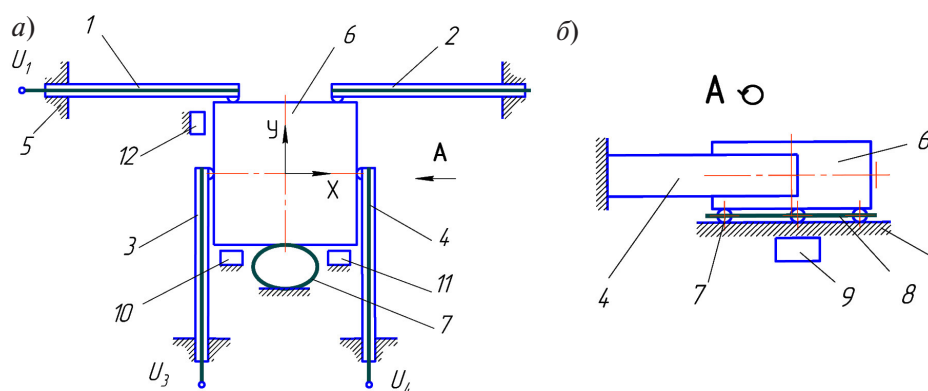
Схема двухкоординатного столика: а) вид сверху; б) вид по стрелке А
